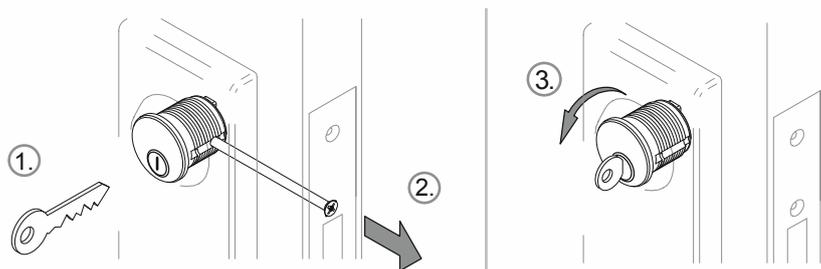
Desmontaje del cilindro antiguo: perfil de cerradura empotrable
